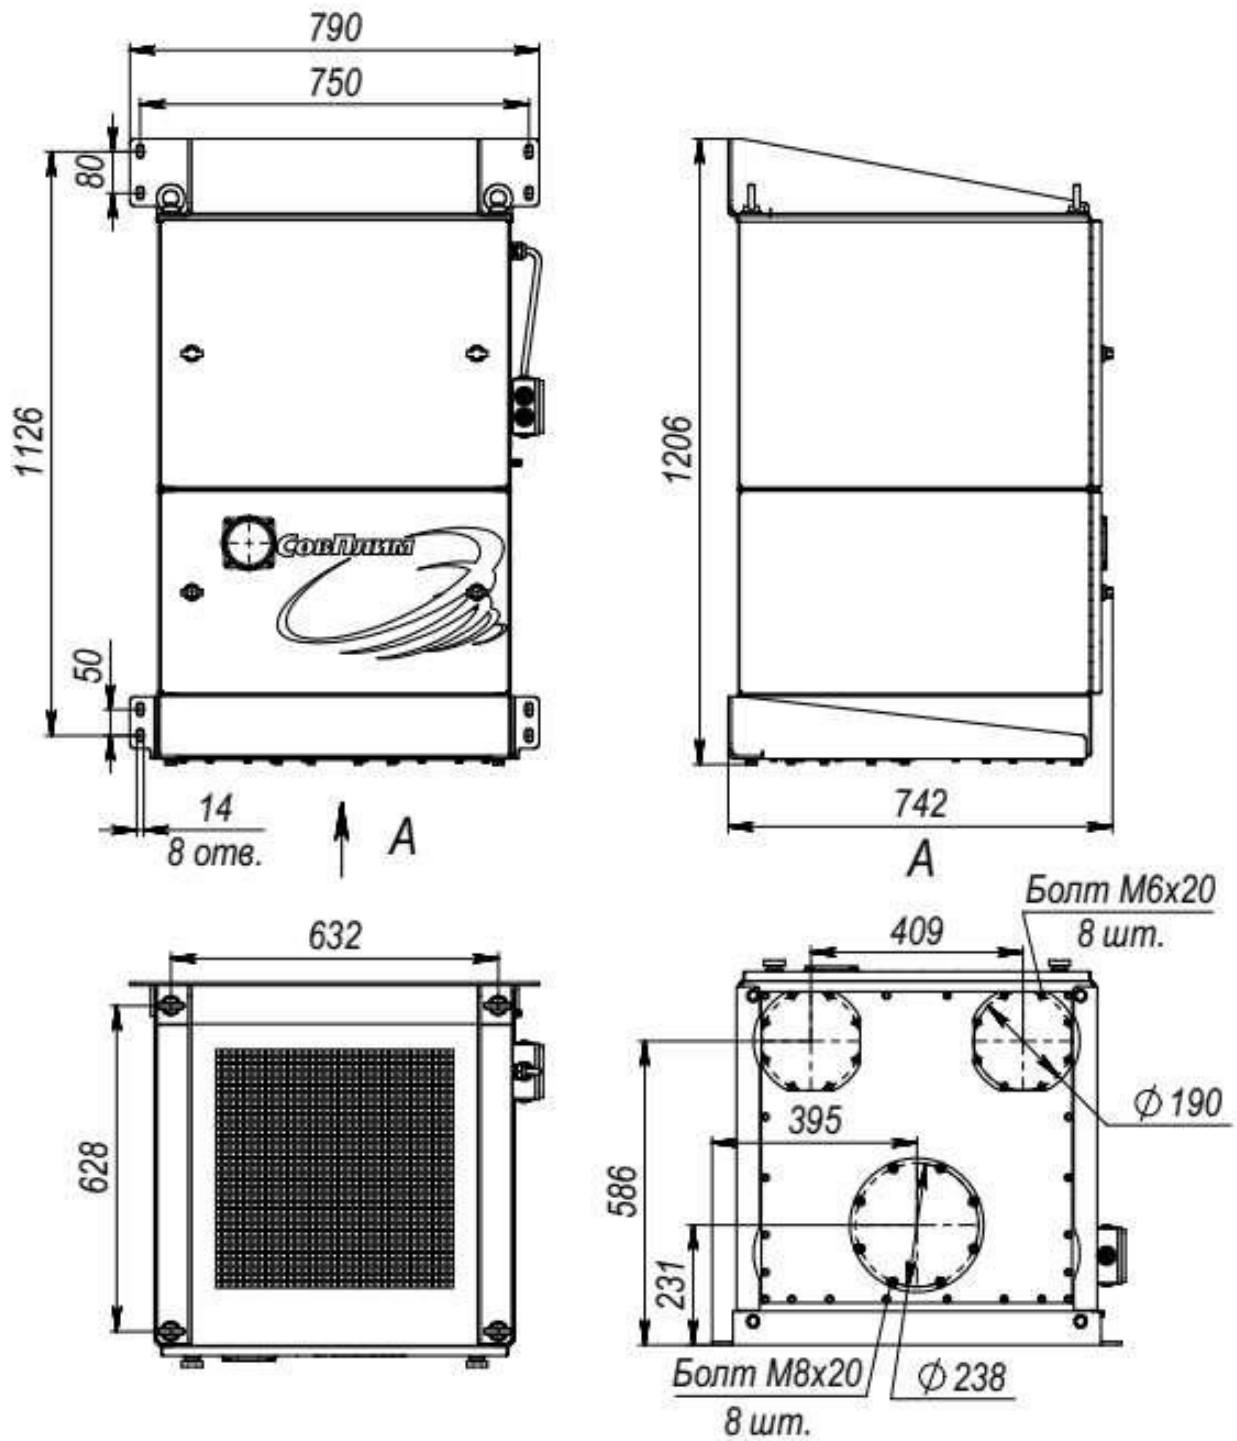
Габаритные размеры фильтра MF-H-31-F6
